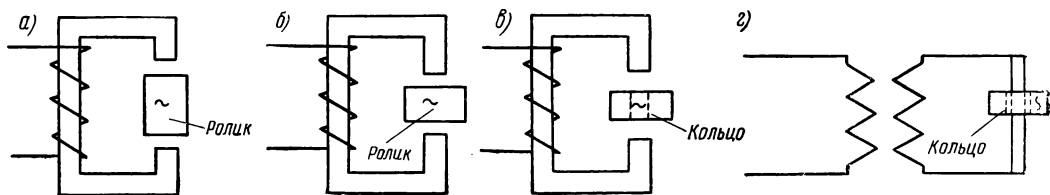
Схемы намагничивания ролика и кольца роликового подшипника:
